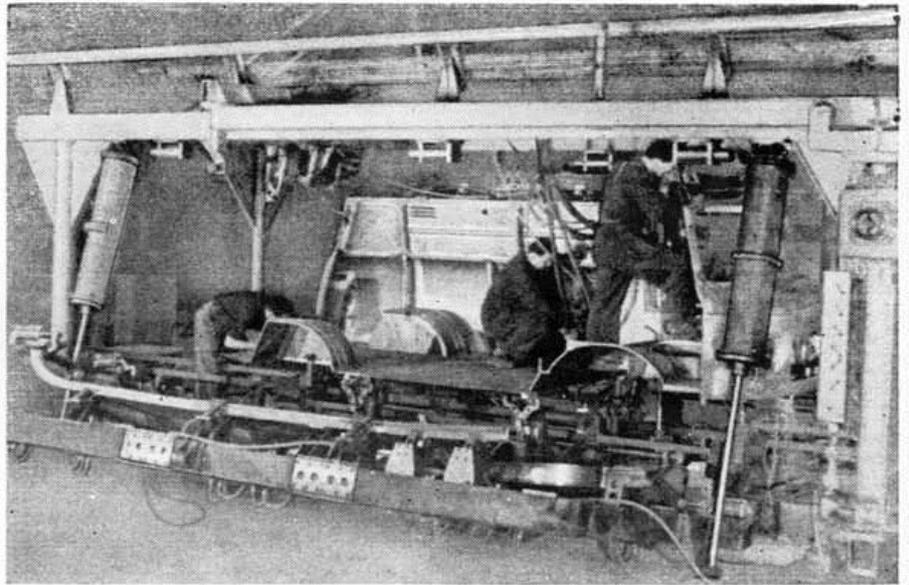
Schweißvorrichtung für das Zusammenfügen der Seitenteile mit der Bodengruppe und der Vorderwand
